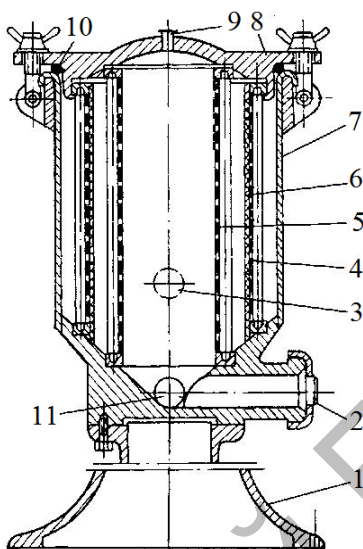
Закрытый цилиндрический фильтр для молока
